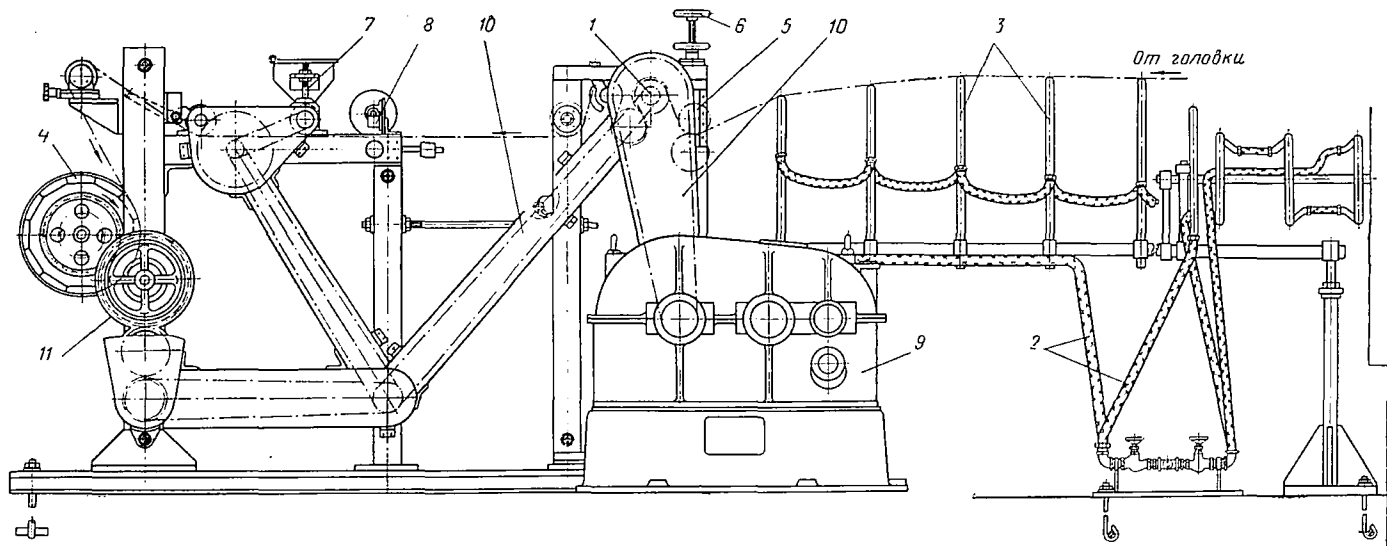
Устройство для приемки, вытягивания и намотки пленки
